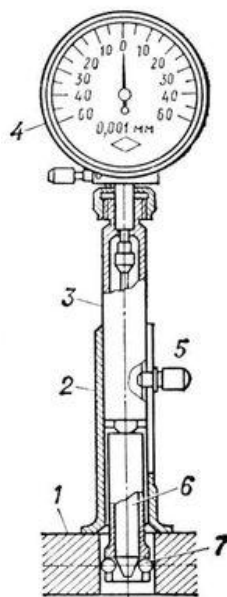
Шариковый индикаторный нутромер для измерения малых отверстий:
